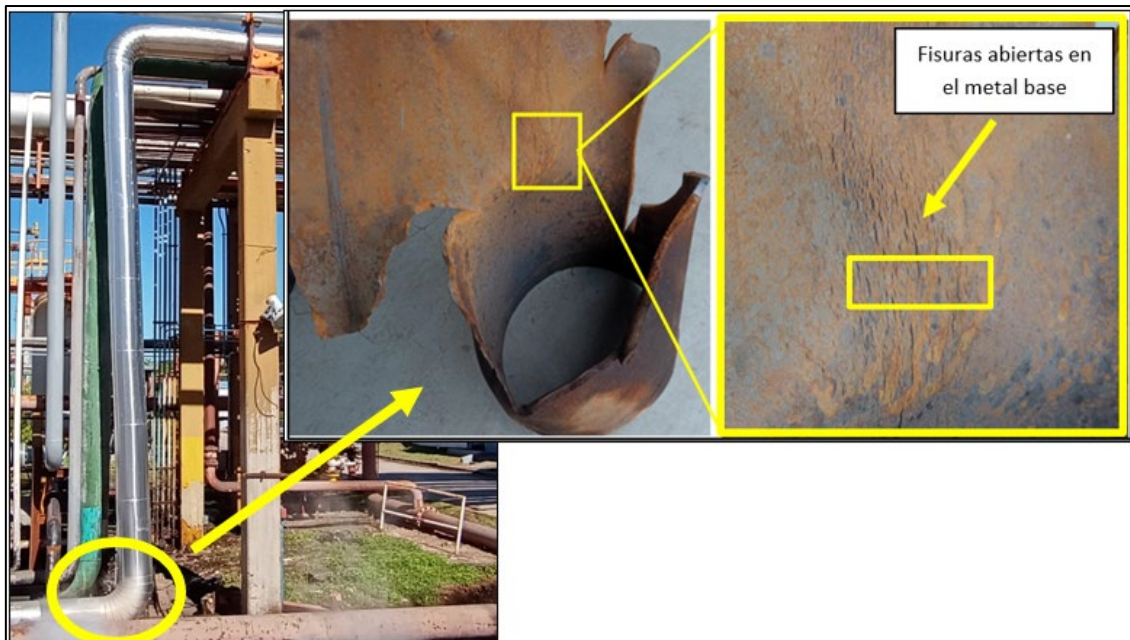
Codo inferior. Se observaron gran cantidad de fisuras preexistentes que se abrieron por la deformación.
